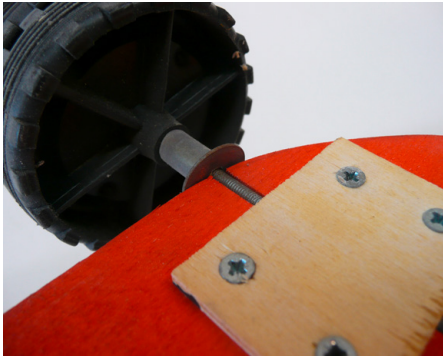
| Achse im genuteten Brett und Abstandhalter durch einen Kunststoffrohrabschnitt
